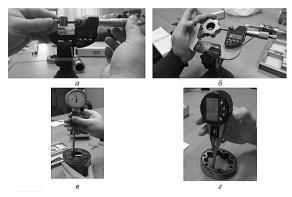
Измерение изношенных деталей героллерного гидромотора Danfoss OMR 100: a- ролик; 6- звезда; 8- корпус; 2- обойма
